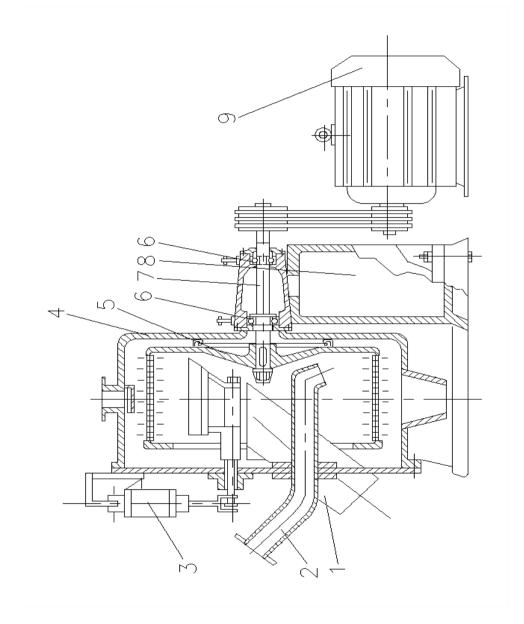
Конструктивная схема центрифуги типа ФГН с консольным ротором:
